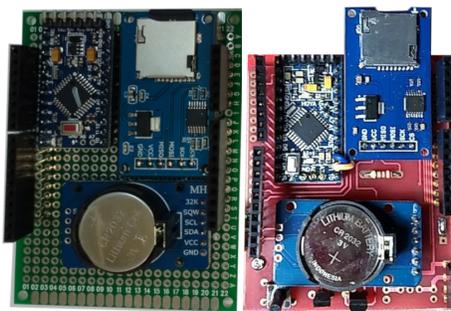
Datalogger, sobre protoboard (izq.) y montado en PCB (der.).
